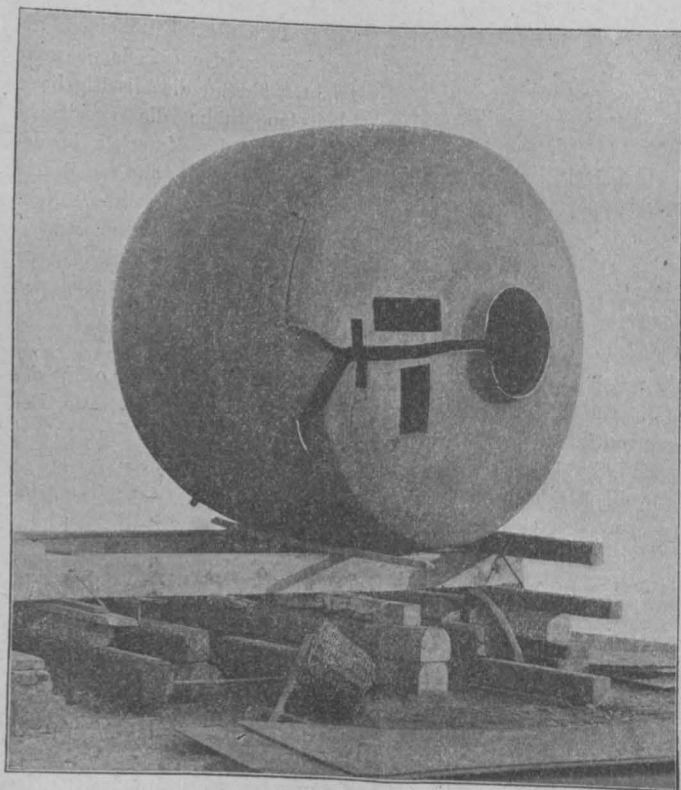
Geschweißter Kessel nach dem Zerspringen mit innerem Wasserdruck (Die rechteckigen Ausschnitte sind durch die Entnahme von Probematerial entstanden)
